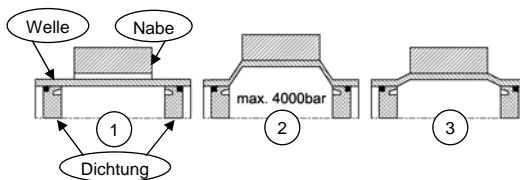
Prinzipskizze des Innenhochdruckfügens einer Welle-Nabe-Verbindung
